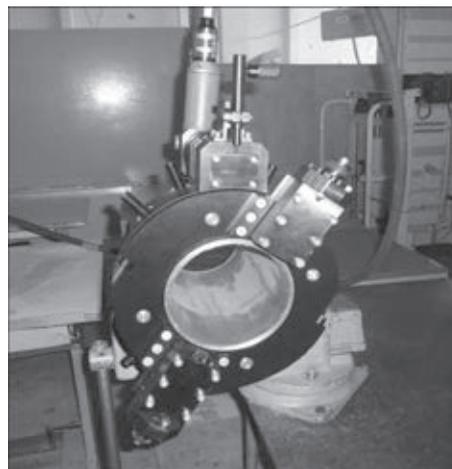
Общий вид опытного образца трубореза ТТЦ 660 УЗ.1
